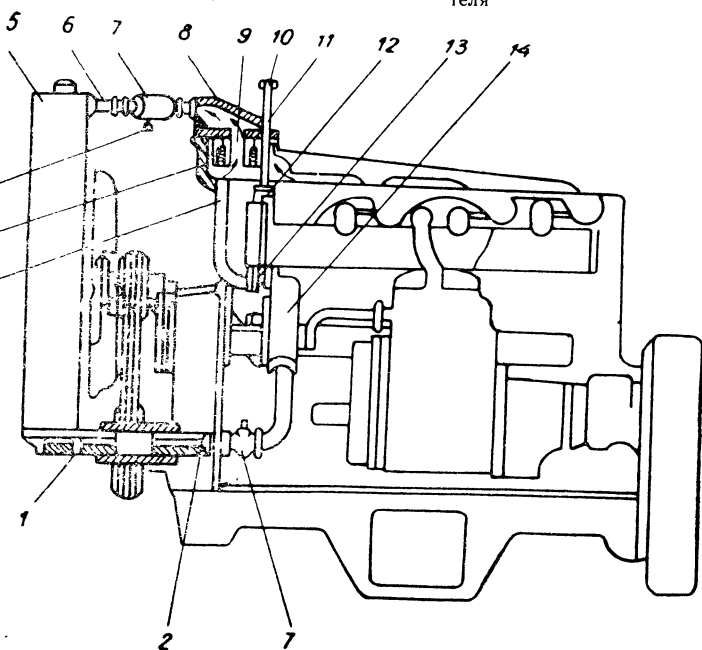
Схема отключения радиатора от двигателя КДМ-100:
